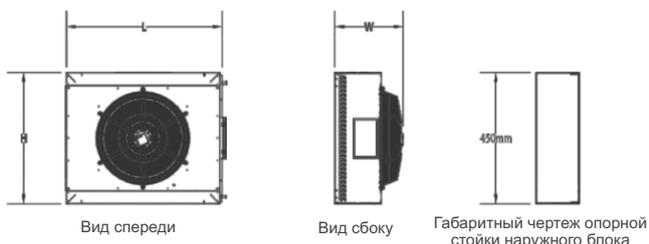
Конструктивный чертеж (с одним вентилятором)
